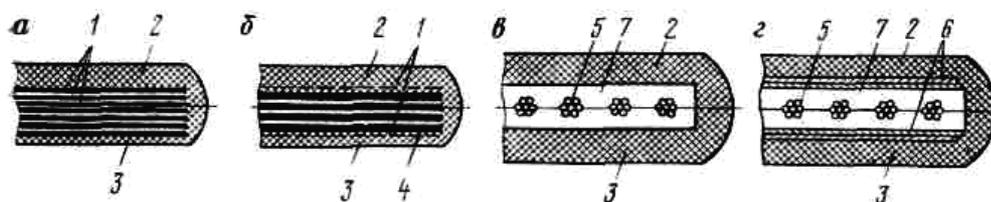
Конструкция конвейерных лент: 1 — прокладки; 2 — верхняя рабочая обкладка; 3 — нижняя обкладка; 4 — брекерная ткань; 5 — трос; 6 — предохранительная прокладка; 7 — резиновый наполнитель
